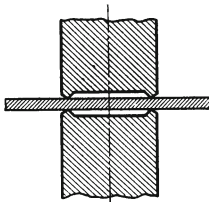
Ringbuckel, gedreht, z. B. gleichzeitiges vakuumdichtes Anschweißen zweier Rundstählen an ein Blech (nach dem Schweißen Bohrung).
